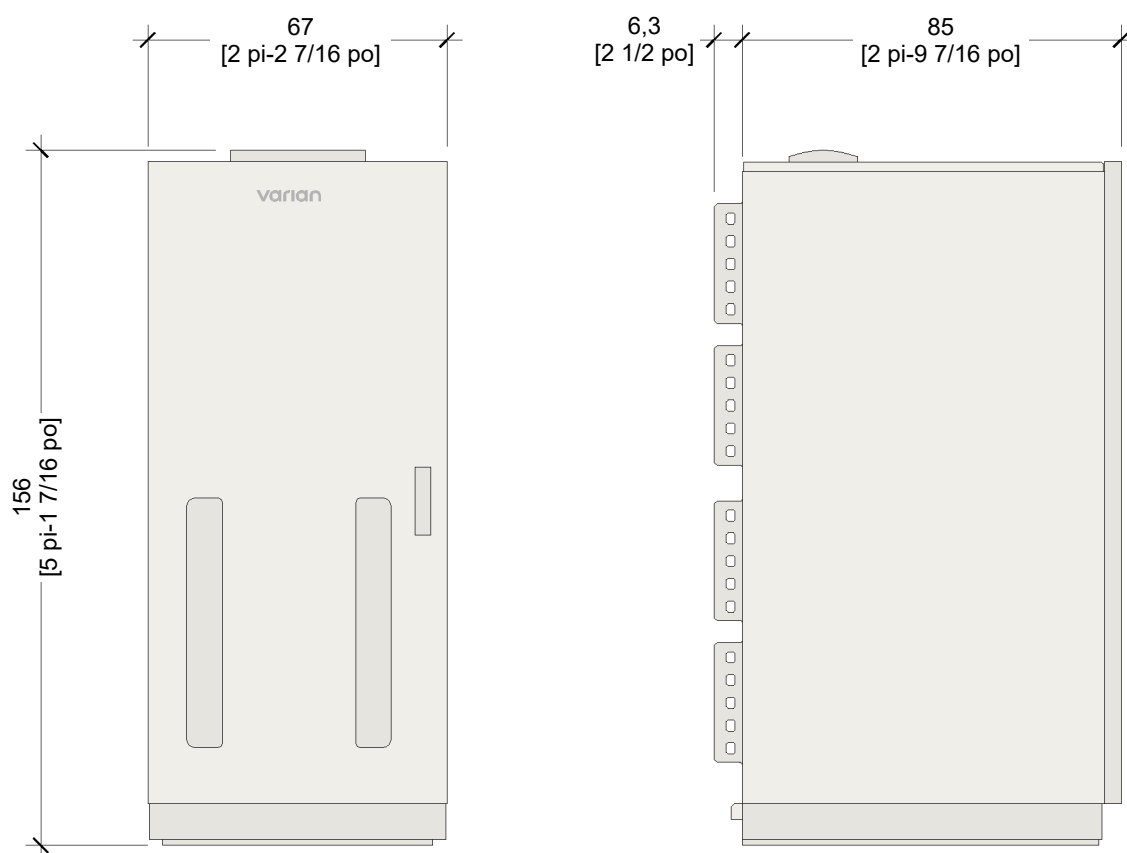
Armoire de la console (vue de face et vue latérale)
